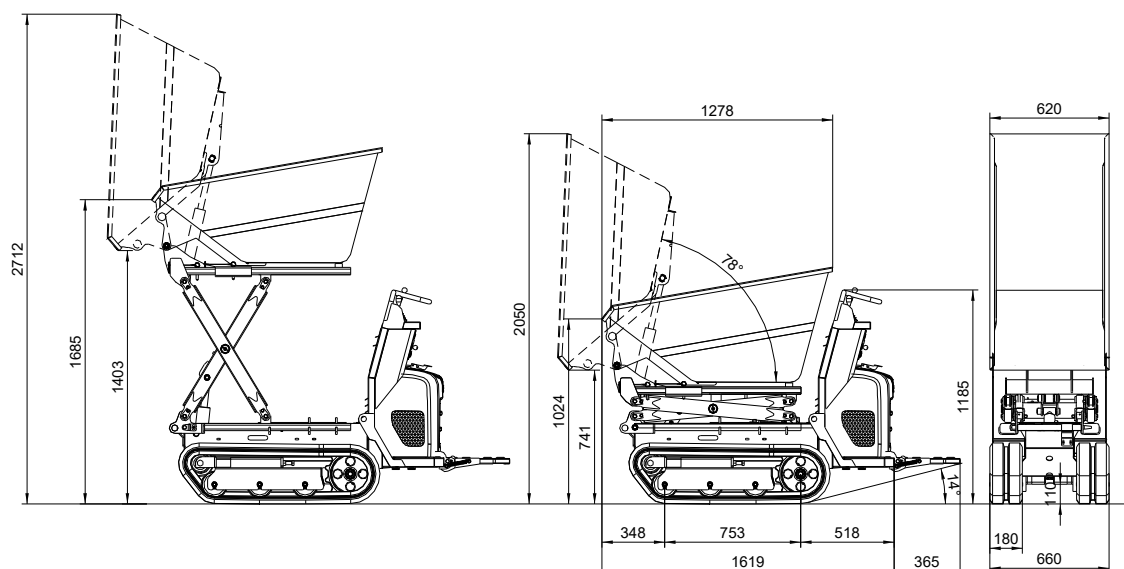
Køretøjets dimensioner (type DT05-D med løftbart tippelad)
